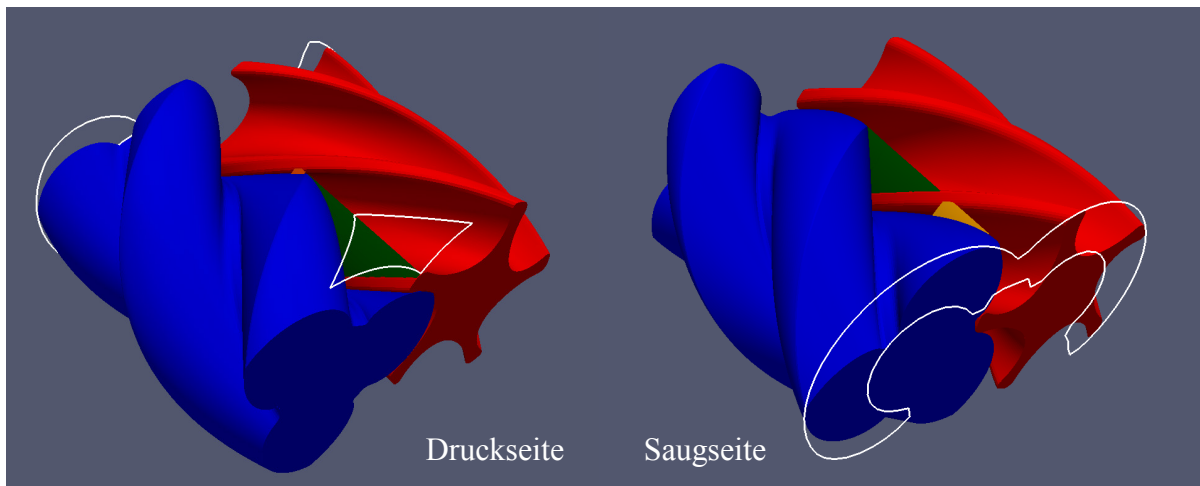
Exemplarische Darstellung des Profileingriffsspalt einer Schraubenmaschine auf dem Haupt- und Nebenrotor
